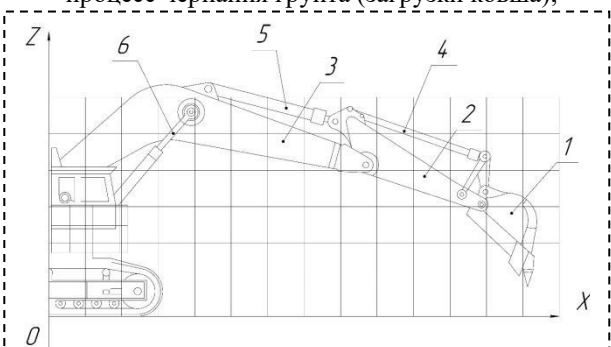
Компоненты рабочего оборудования гидравлического экскаватора типа «обратная лопата» 1 – ковш, 2 – рукоять, 3 – стрела; 4 – гидроцилиндр поворота ковша, 5 – гидроцилиндр поворота рукояти, 6 – гидроцилиндр поворота стрелы.
